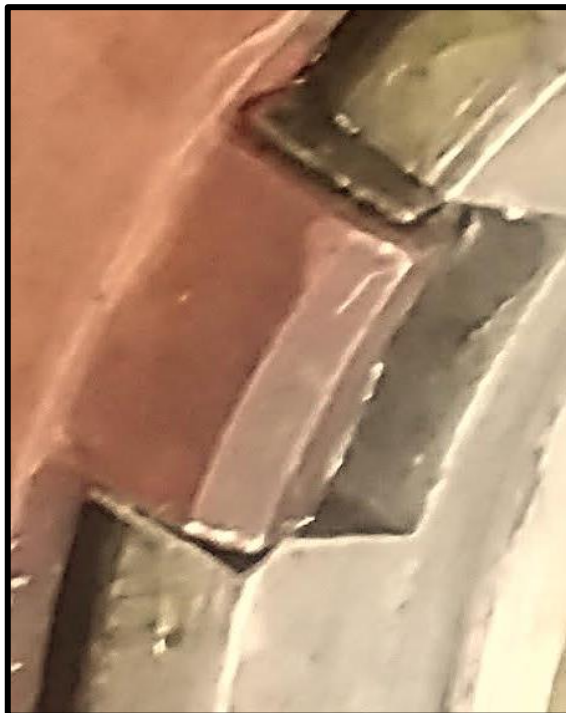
Montaje de la Race Center en el Blade and bushes assembly
